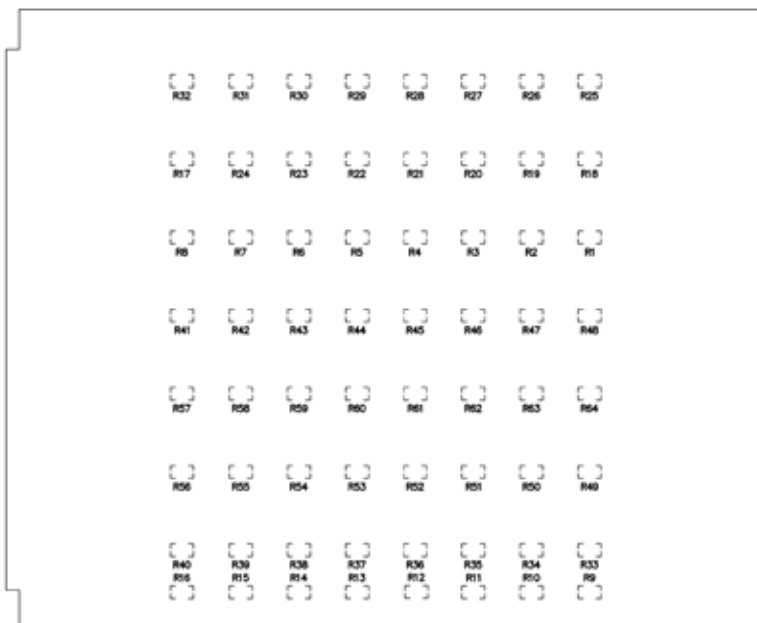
PXI 31128 Aufsatzboard Version 2 – Top Layer
